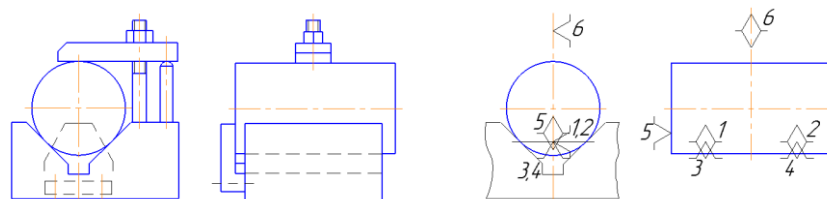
Установка вала в призме: 1–6 – опорные точки
